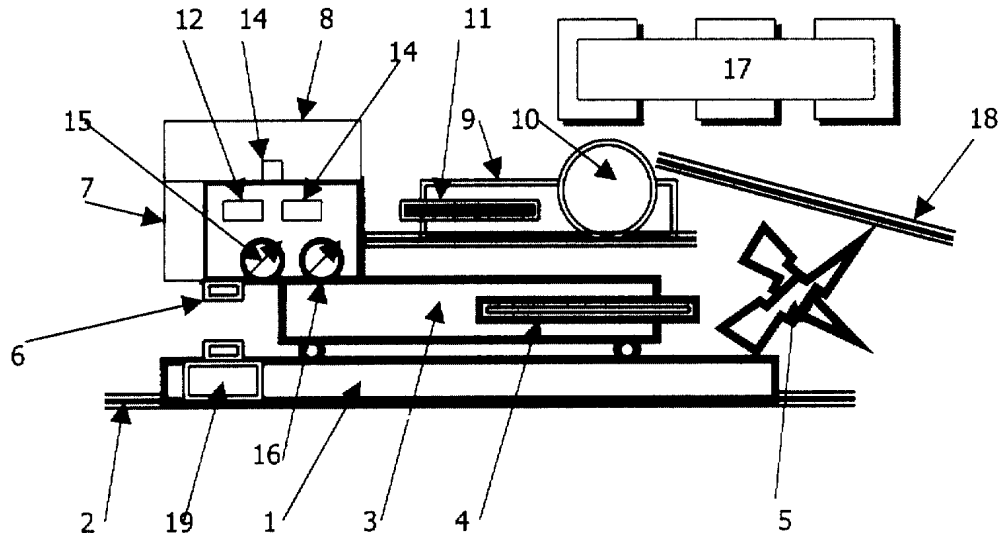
Схема установки для изготовления шаров из асбоволокнита
